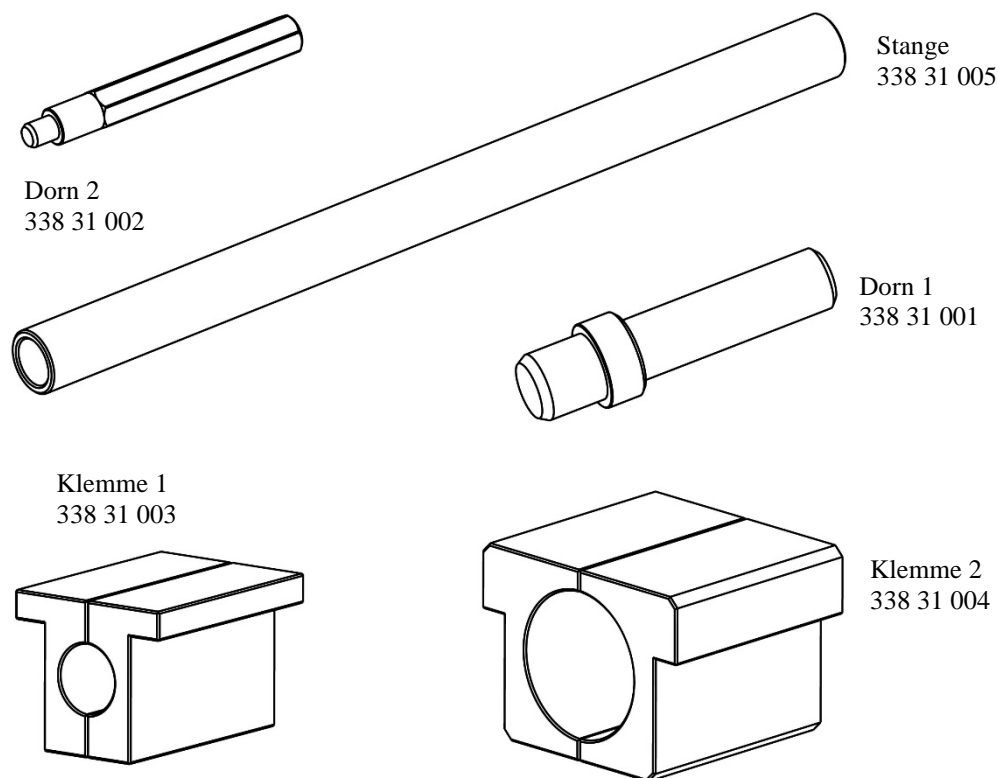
Spezialwerkzeuge für die Montage oder die Demontage der Rückzugstütze PN 67 C
